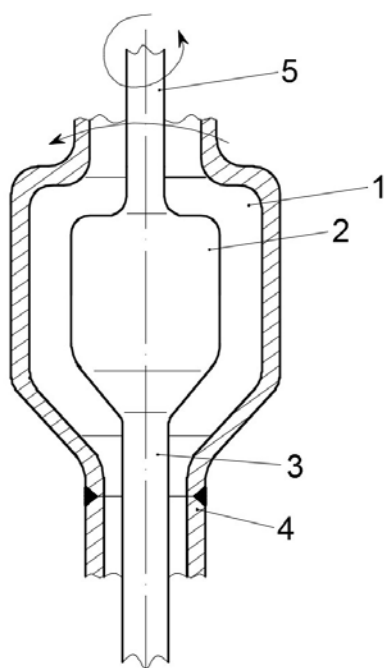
Рабочие камеры: 1 – основная рабочая камера; 2 – дополнительная рабочая камера; 3 – газовод для подачи сжатого воздуха к выхлопным отверстиям нижнего газового импульса; 4 – штанговый корпус; 5 – хвостовик
